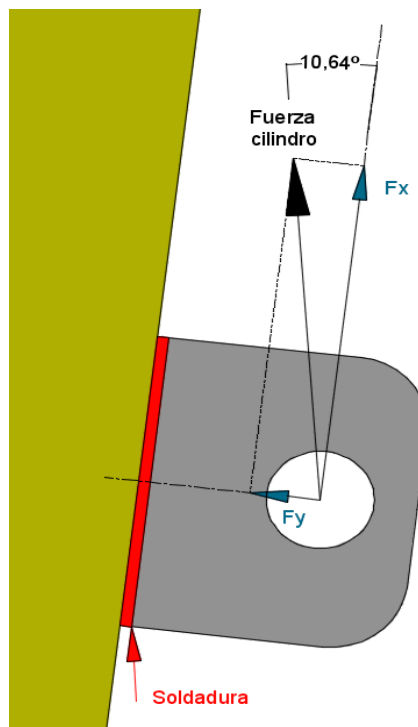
Descomposición de fuerzas para las soldaduras
